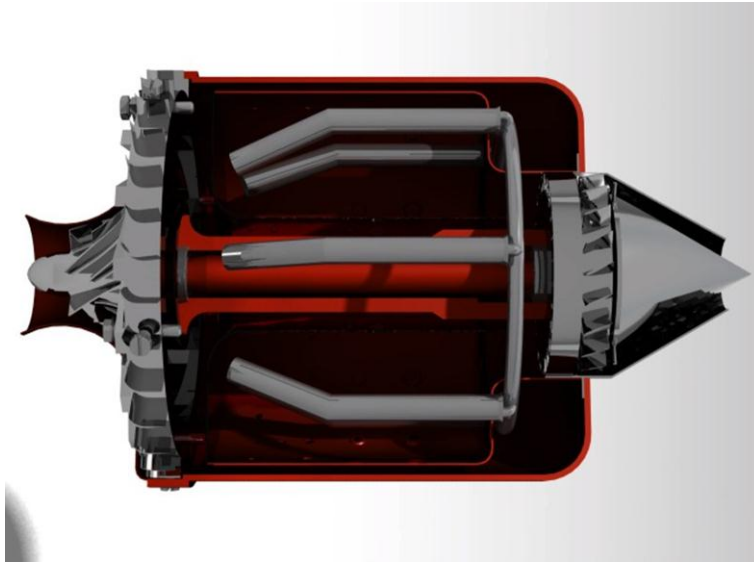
Vista lateral con corte del ensamble del Motor GMMO-1524-A.
